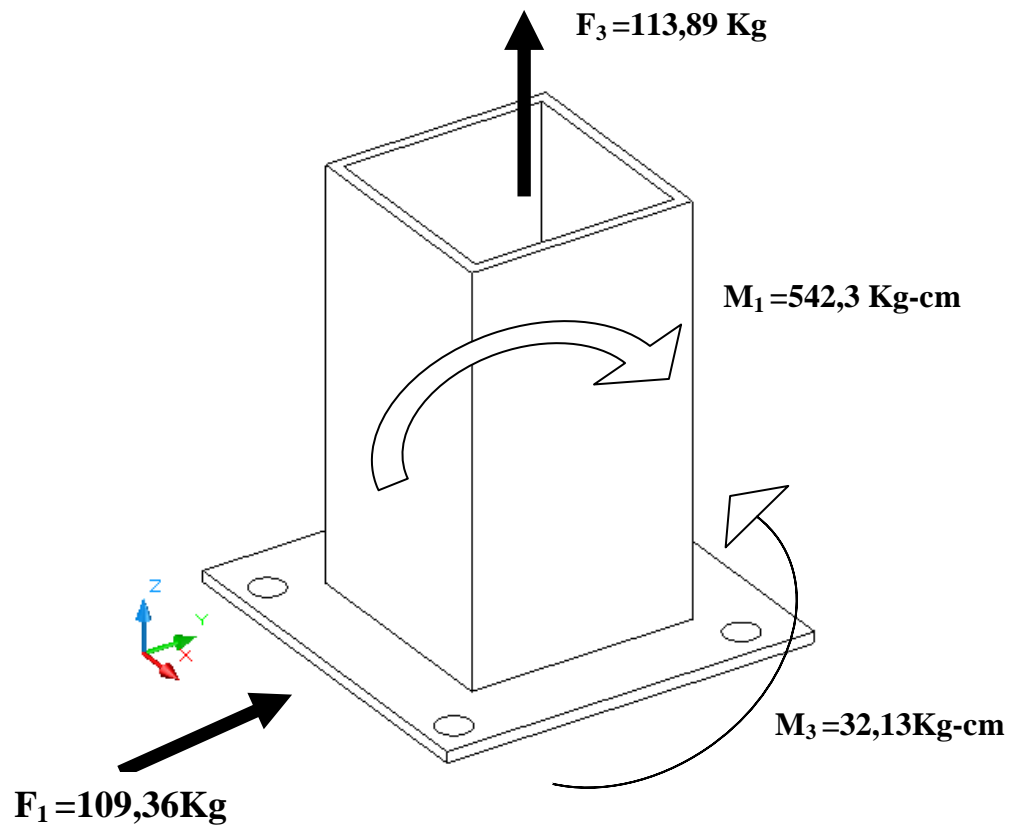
Cargas aplicadas en placa base de la estructura.
